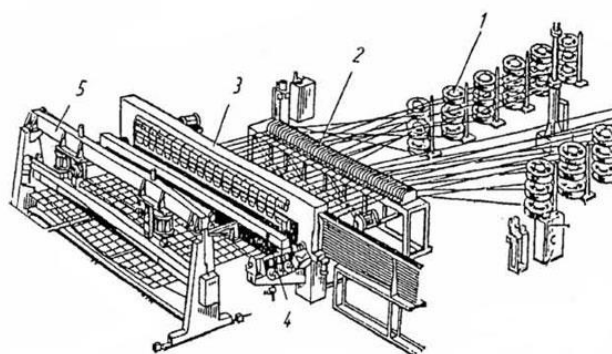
Изготовление сеток на многоточечной машине (Примечание: 1 – бухта арматурной стали Ø 5–10 мм; 2 – распределение арматуры по проектным размерам; 3 – укладка поперечных стержней; 4 – сварка 1–4 рядов; 5 – резка сетки по длине)
